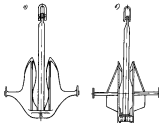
Якорь Матросова. а — литейный, б — сварной.
